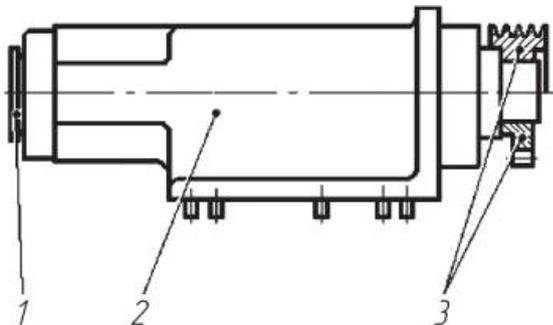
Расточная бабка: 1 — шпиндель; 2 — корпус; 3 — приводной шкив или зубчатое колесо.
